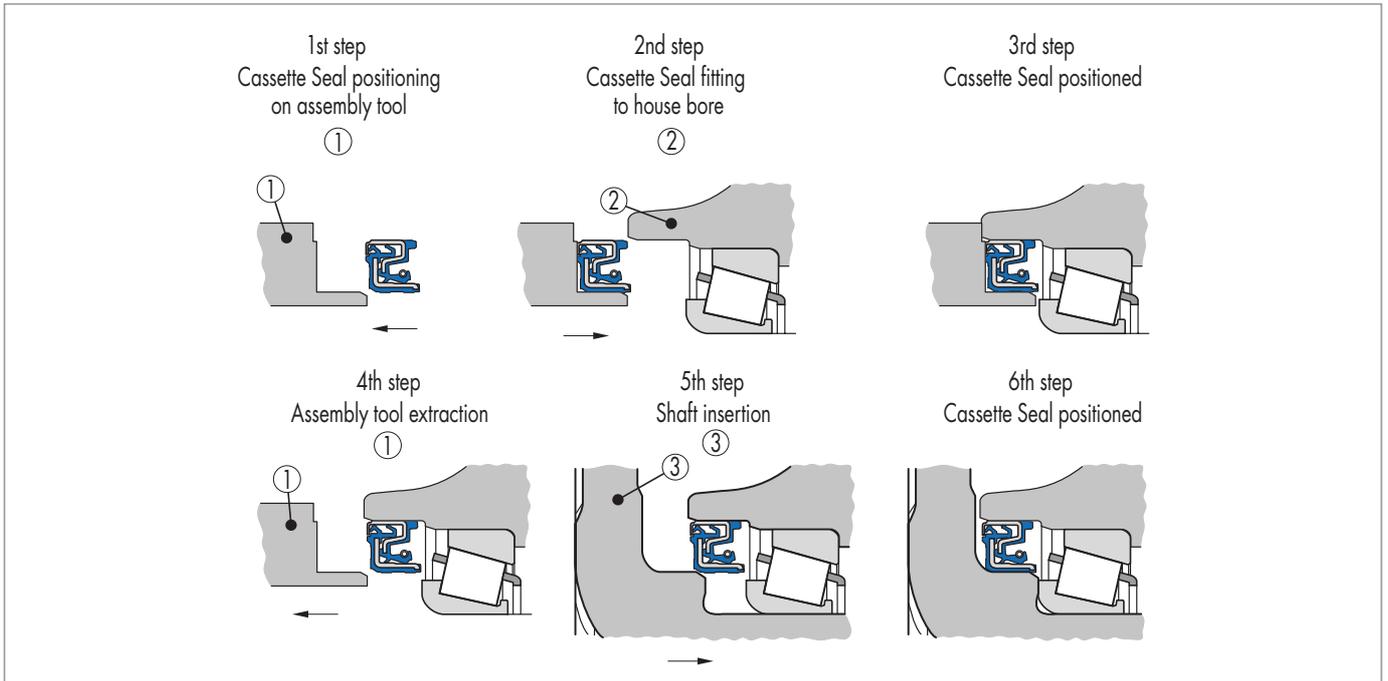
Montage von Simmerring Cassette Seal – Fall B (ohne „bearing stop“) / Yağ Halkası Cassette Seal Montajı – Durum B („bearing stop“ haric) / Montaż uszczelnienia typu kaseta – przypadek B (bez „bearing stop“) / Монтаж кассетного уплотнения – вариант В (без «упора в подшипник»)
